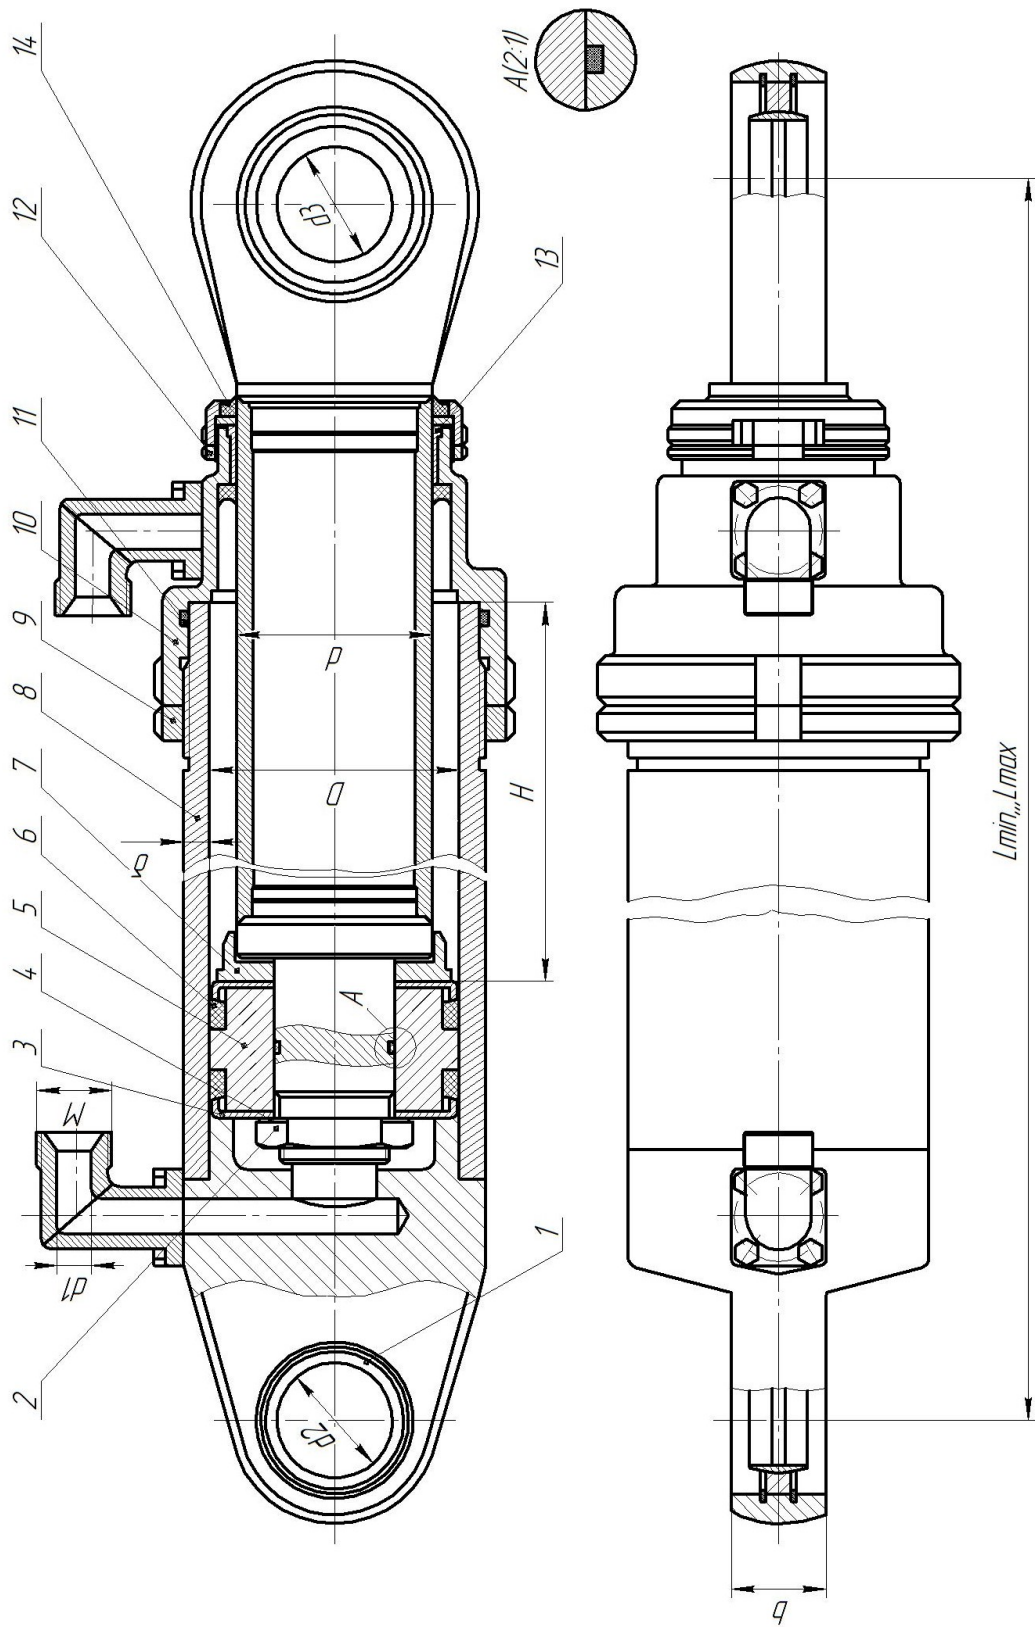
Гідроциліндр: 1 – проушина циліндру; 2 – гайка; 3 – упор; 4 – шайба стопорна; 5 – поршень; 6 – манжета; 7 – конус; 8 – гільза циліндру; 9 – гайка; 10 – кришка; 11 – кльце; 12 – гайка; 13 – втулка; 14 – грязезйомник
